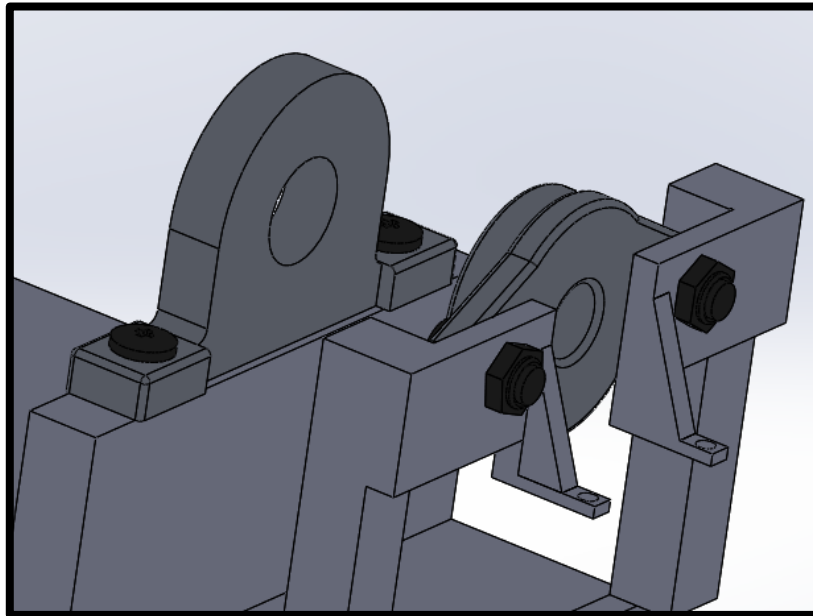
Detalle de los rodamientos A y B montados. Fuente: Propia.
